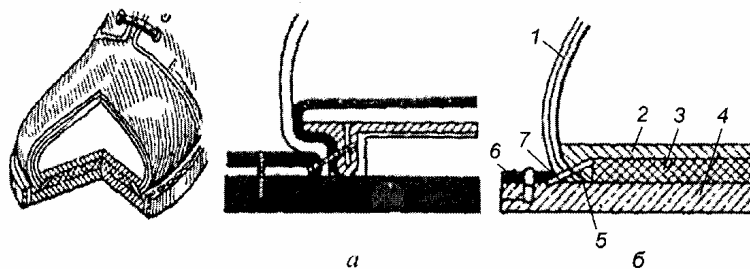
Схема рантового метода крепления подошвы со стелькой с искусственной (а) и натуральной (б) губой:
